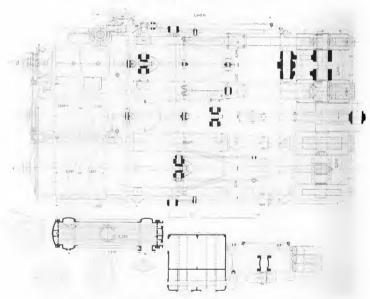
Draufsicht und Schnitte. — Masstab 1:20.
